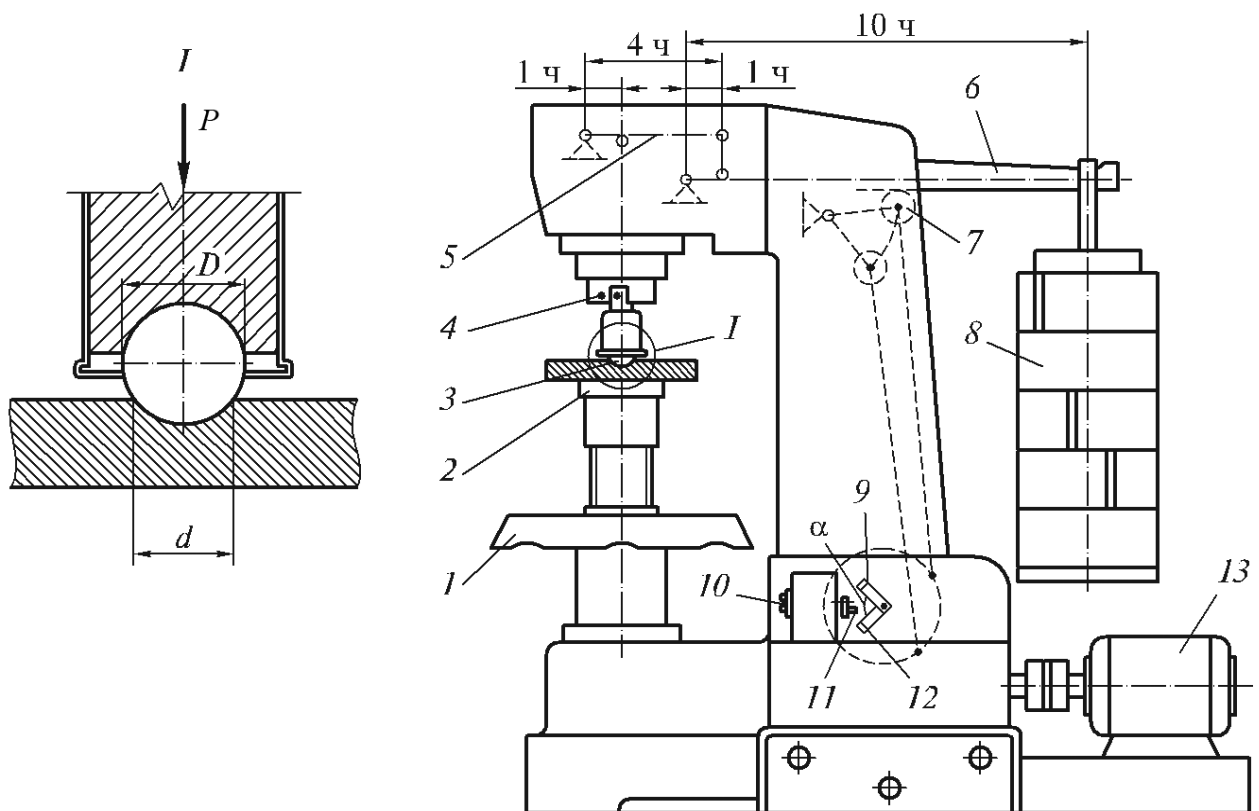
Схема пресса Бринелля: 1 — маховик; 2 — опора образца; 3 — шарик; 4 — метки; 5 — рычаг 1:4; 6 — рычаг 1:10; 7 — подвижная опора; 8 — грузы; 9, 12 — кулачки; 10 — кнопка пуска; 11 — концевой переключатель; 13 — электродвигатель; ч — часть
